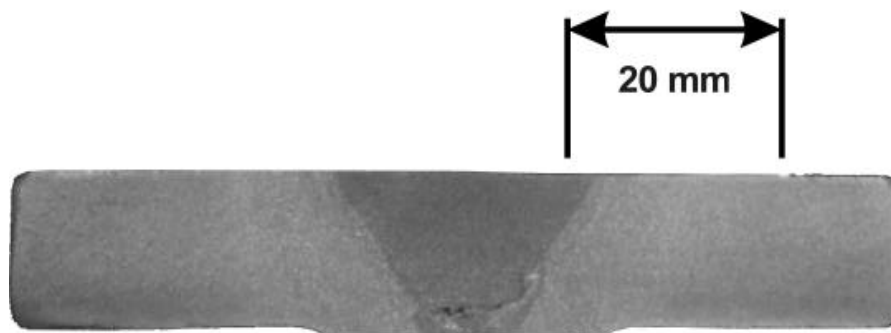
Macrografia de uma junta soldada por fricção radial (ataque 25% de HNO₃ em água).
